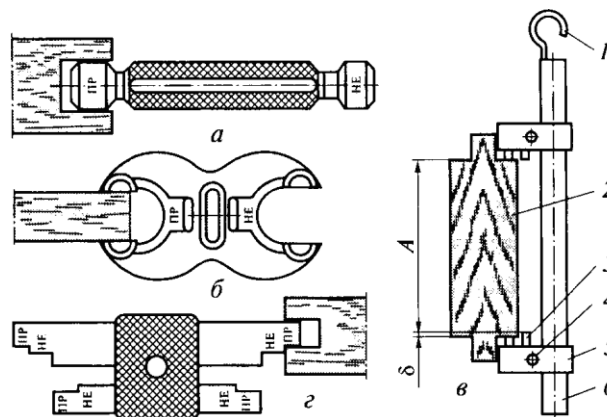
Калібри: *а* – пробка для контролю діаметра отвору; *б* – скоба для контролю товщини деталі; *в* – переналагоджуваний калібр; *г* – комбінований калібр; 1 – гачок; 2 – деталь; 3 – опора; 4 – гвинт; 5 – планка; 6 – стрижень
